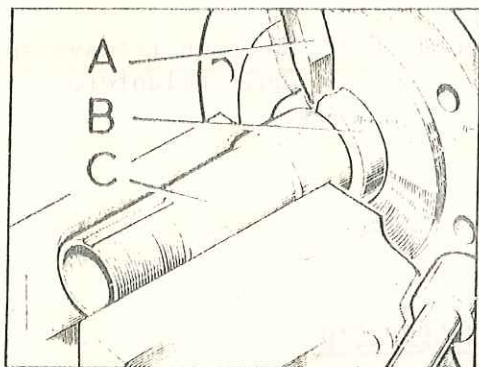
Desmontaje de la pieza distanciadora del cojinete interno
